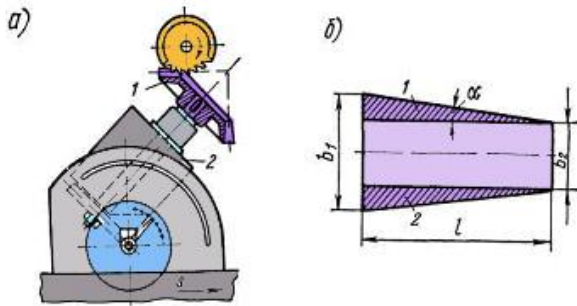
Зубофрезерування конічного зубчастого колеса
